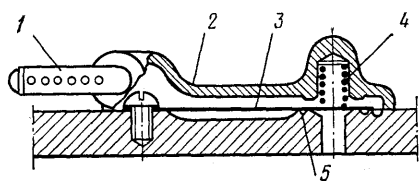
Пластинчатый нагнетательный клапан ротационного компрессора:
